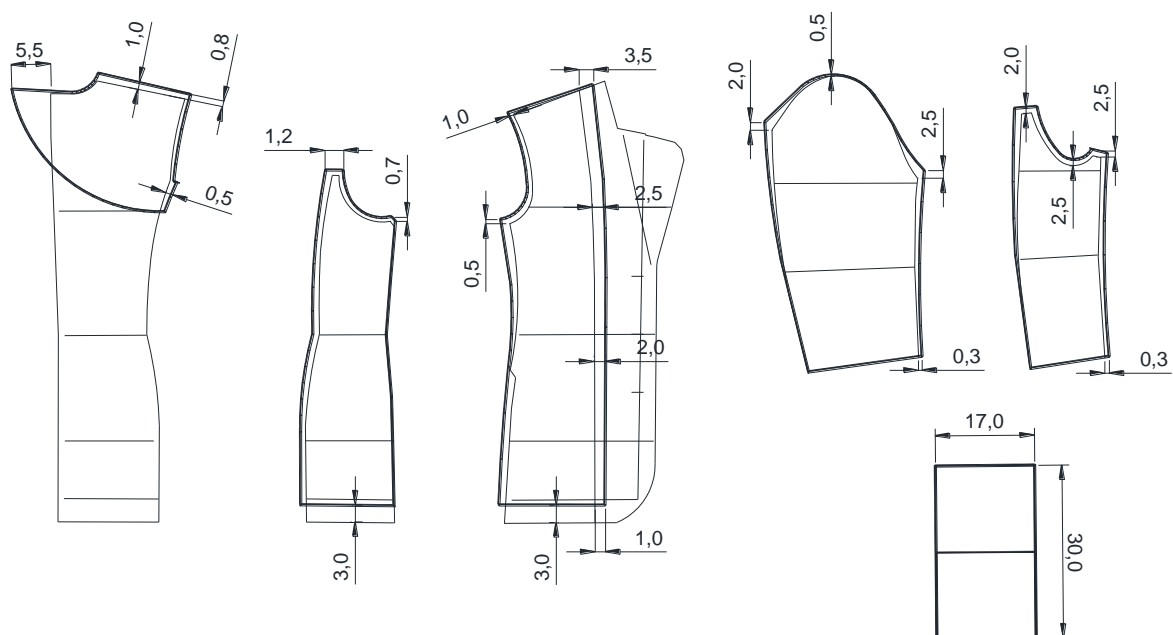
Схеми побудови лекал деталей підкладки
